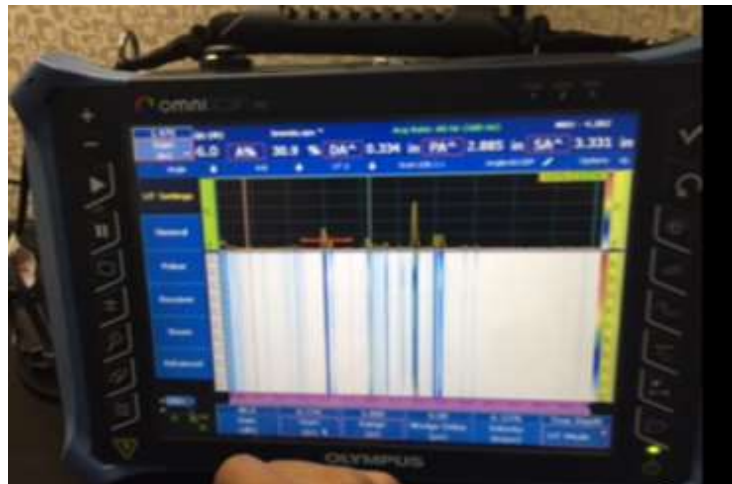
7 Discontinuidad observada en inserto soldado en pantalla de ultrasonido
